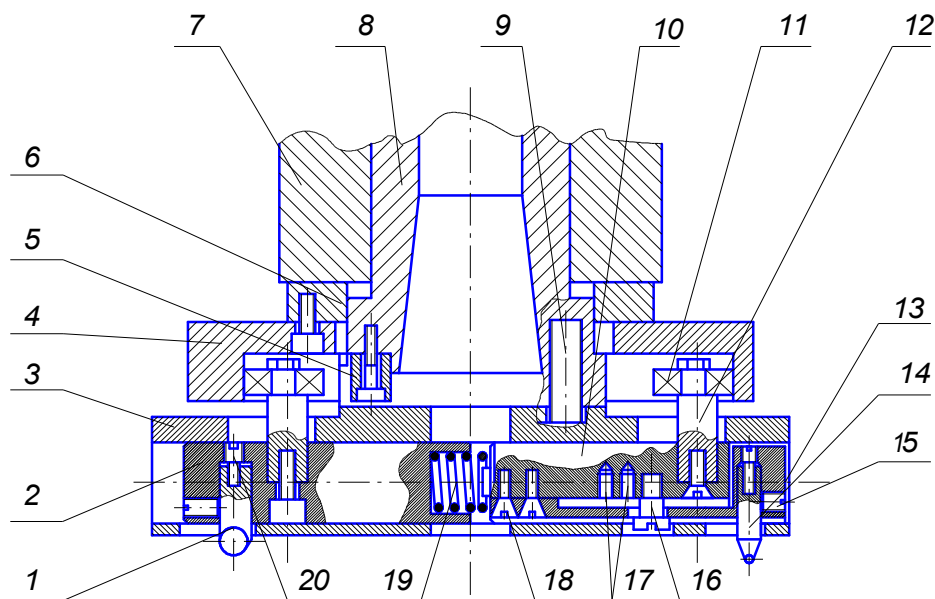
Розріз торцевої фрези для комбінованої обробки
